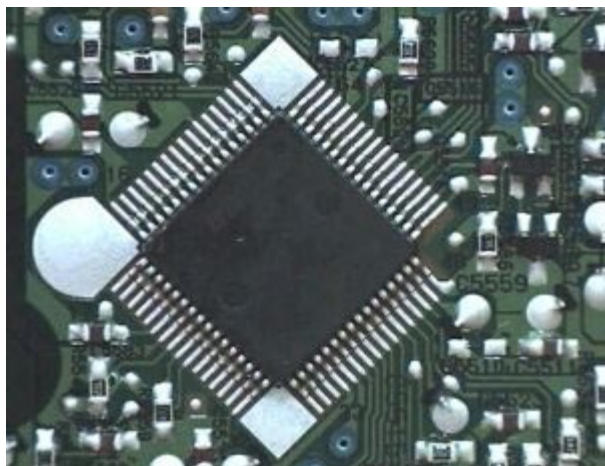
QFP 64 wave soldered, pitch 0,8 mm
